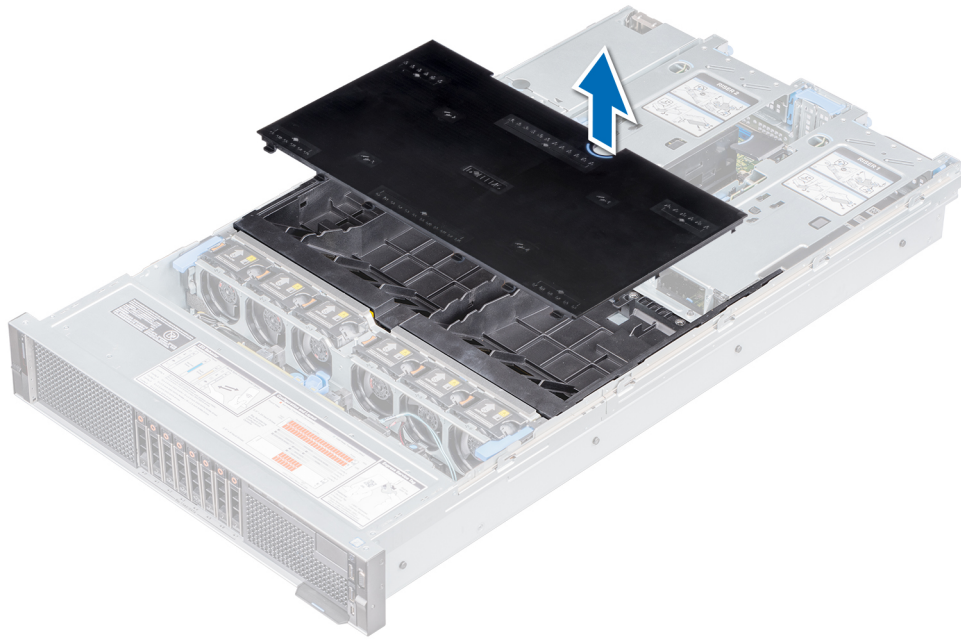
Entfernen der Abdeckung des GPU-Kühlgehäuses
